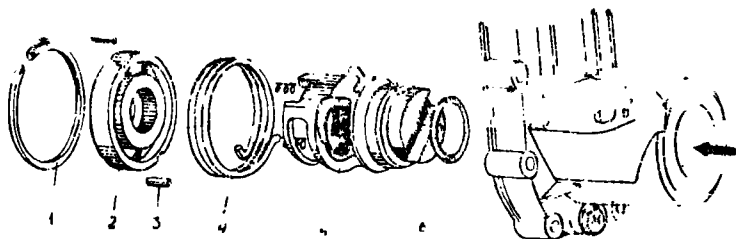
Снятие стопорного кольца, удаление держателя храповика и корпуса пускового механизма.
